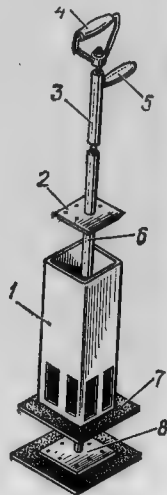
1 — емкость; 2 — фланец уплотнительный; 3 — трубка направляющая; 4 — рукоятка; 5 — ручка; 6 — стержень; 7 — гладители; 8 — фланцы зажимные
